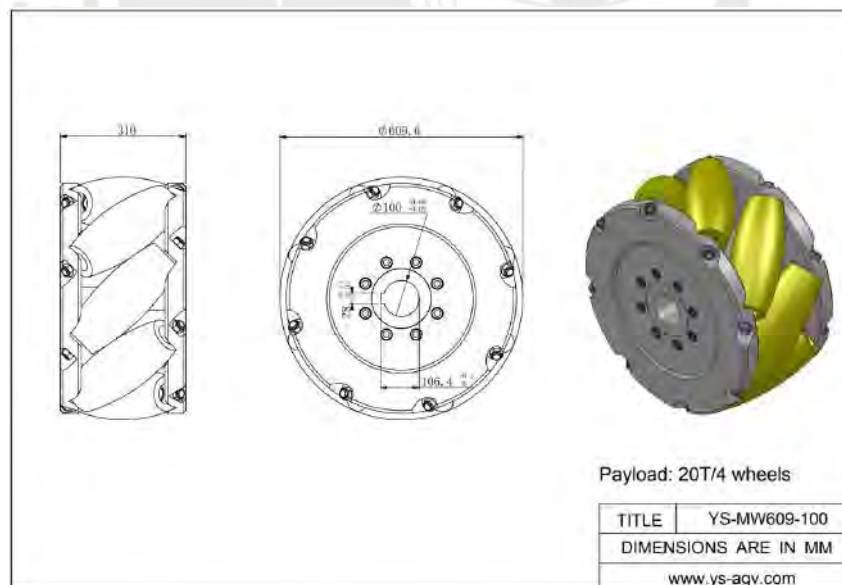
Dimensiones de YS-MW609-100 (YouSheng, 2022)
